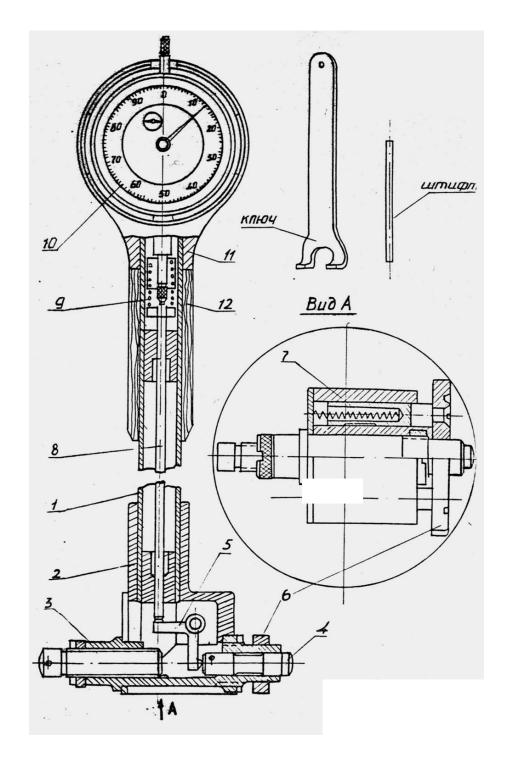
Двухконтактный индикаторный нутромер
